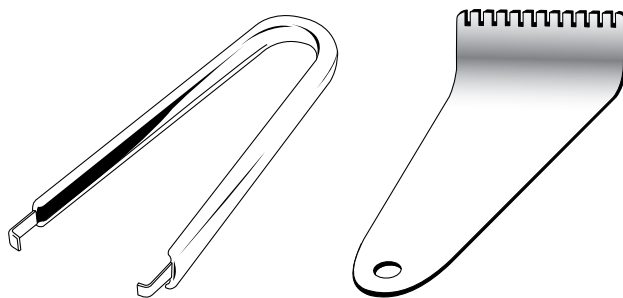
Приспособления для извлечения из гнезд микросхем (слева) и процессоров, кроме ZIF (справа)
